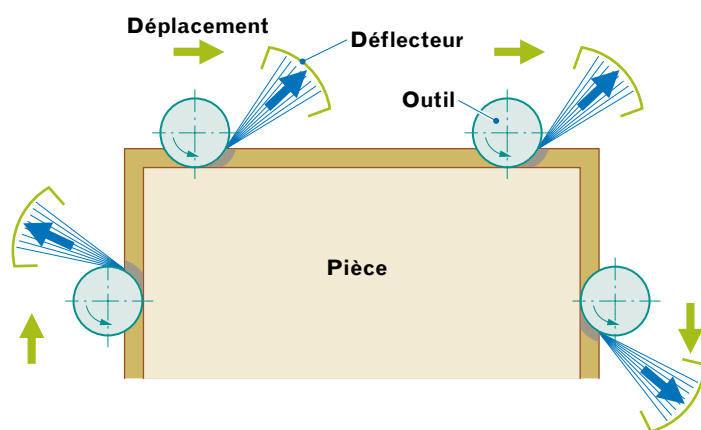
Schéma de principe du dispositif de captage des poussières - Diagram of the principle of the dust exhaust device
